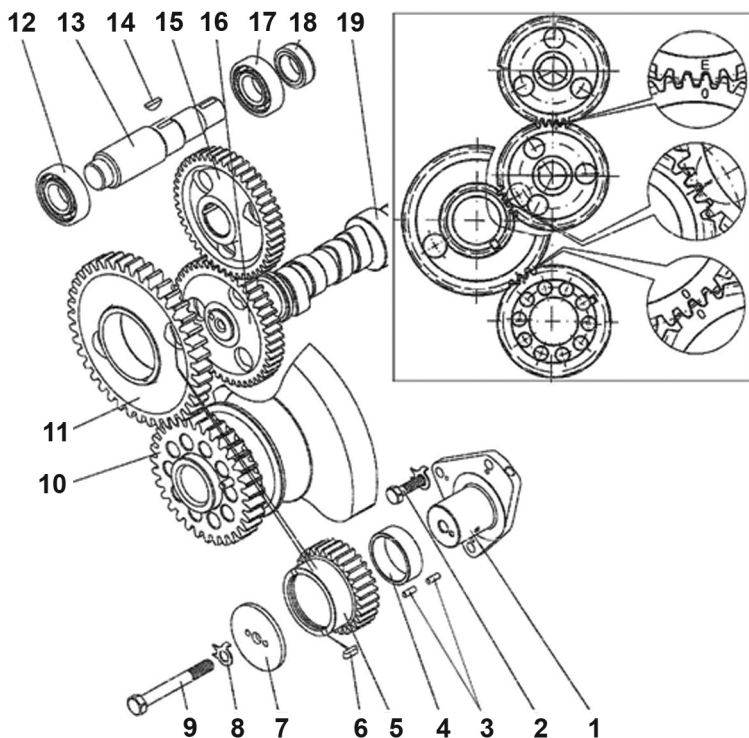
Привод агрегатов (двигатель с картером агрегатов):
